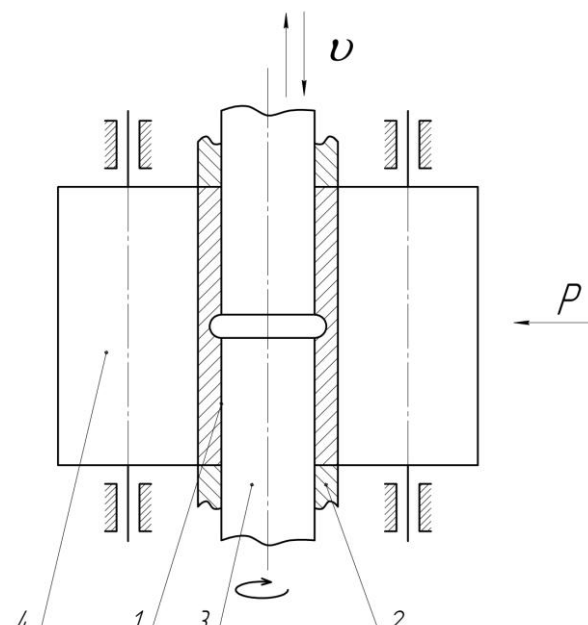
Схема упрочняющего дорнования при ВШ: 1 – заготовка; 2 – упоры; 3 – дорн (пуансон); 4 – валковая матрица
